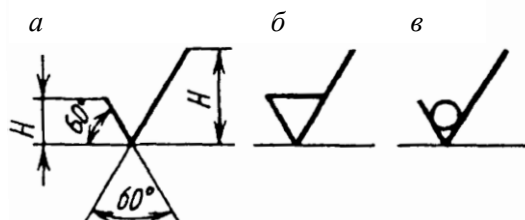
Варианты знаков в обозначении шероховатости поверхности:
